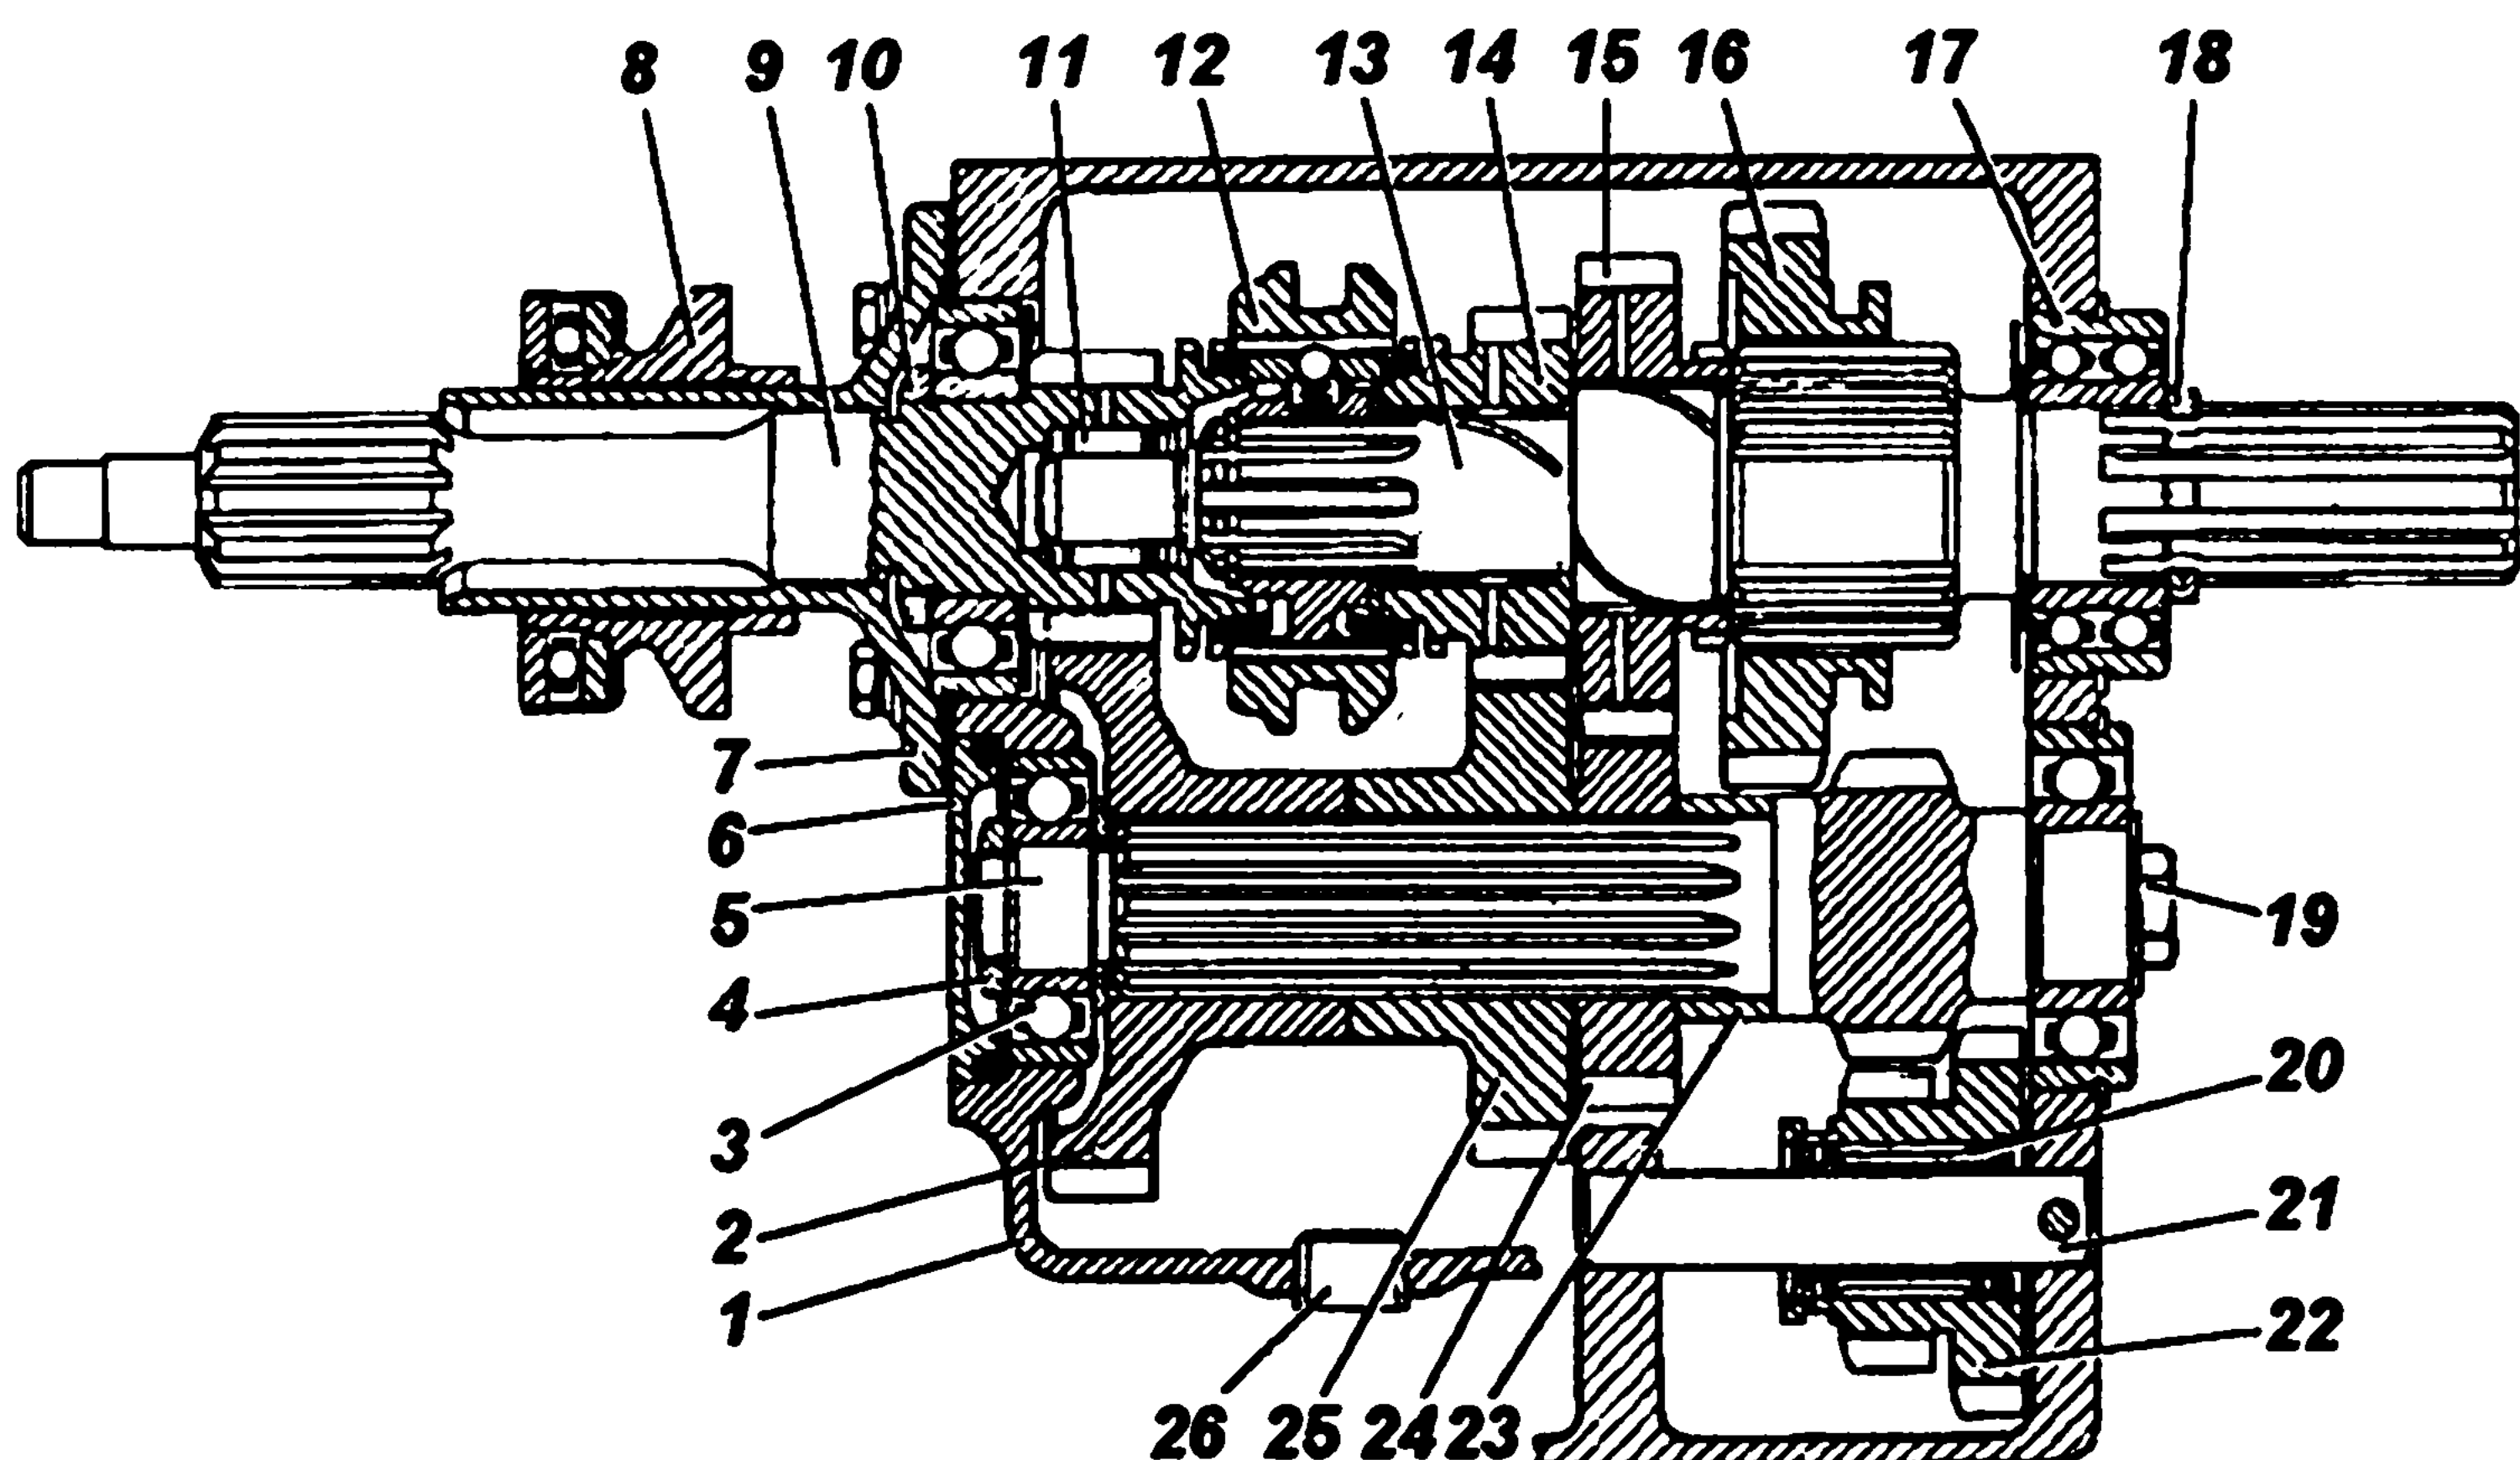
Вариант исполнения коробки передач с синхронизатором только для третьей и четвертой (прямой) передач:
